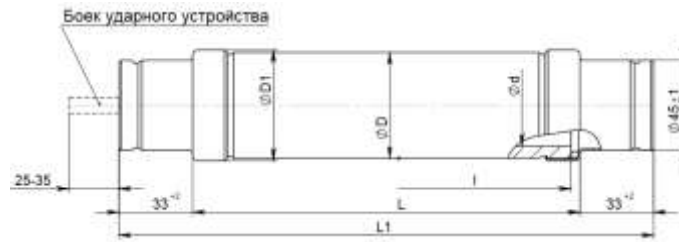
Габаритные, присоединительные и установочные размеры патронов.
